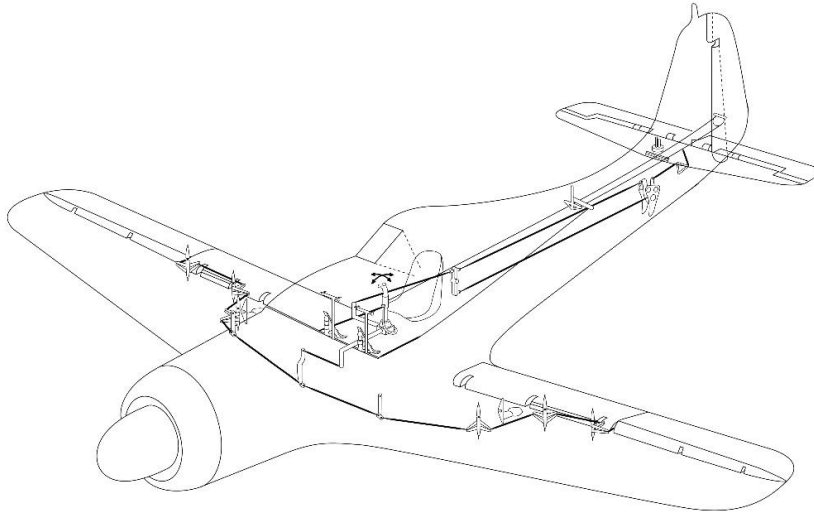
Fw 190 D-9 Flugzeugsteuerung
